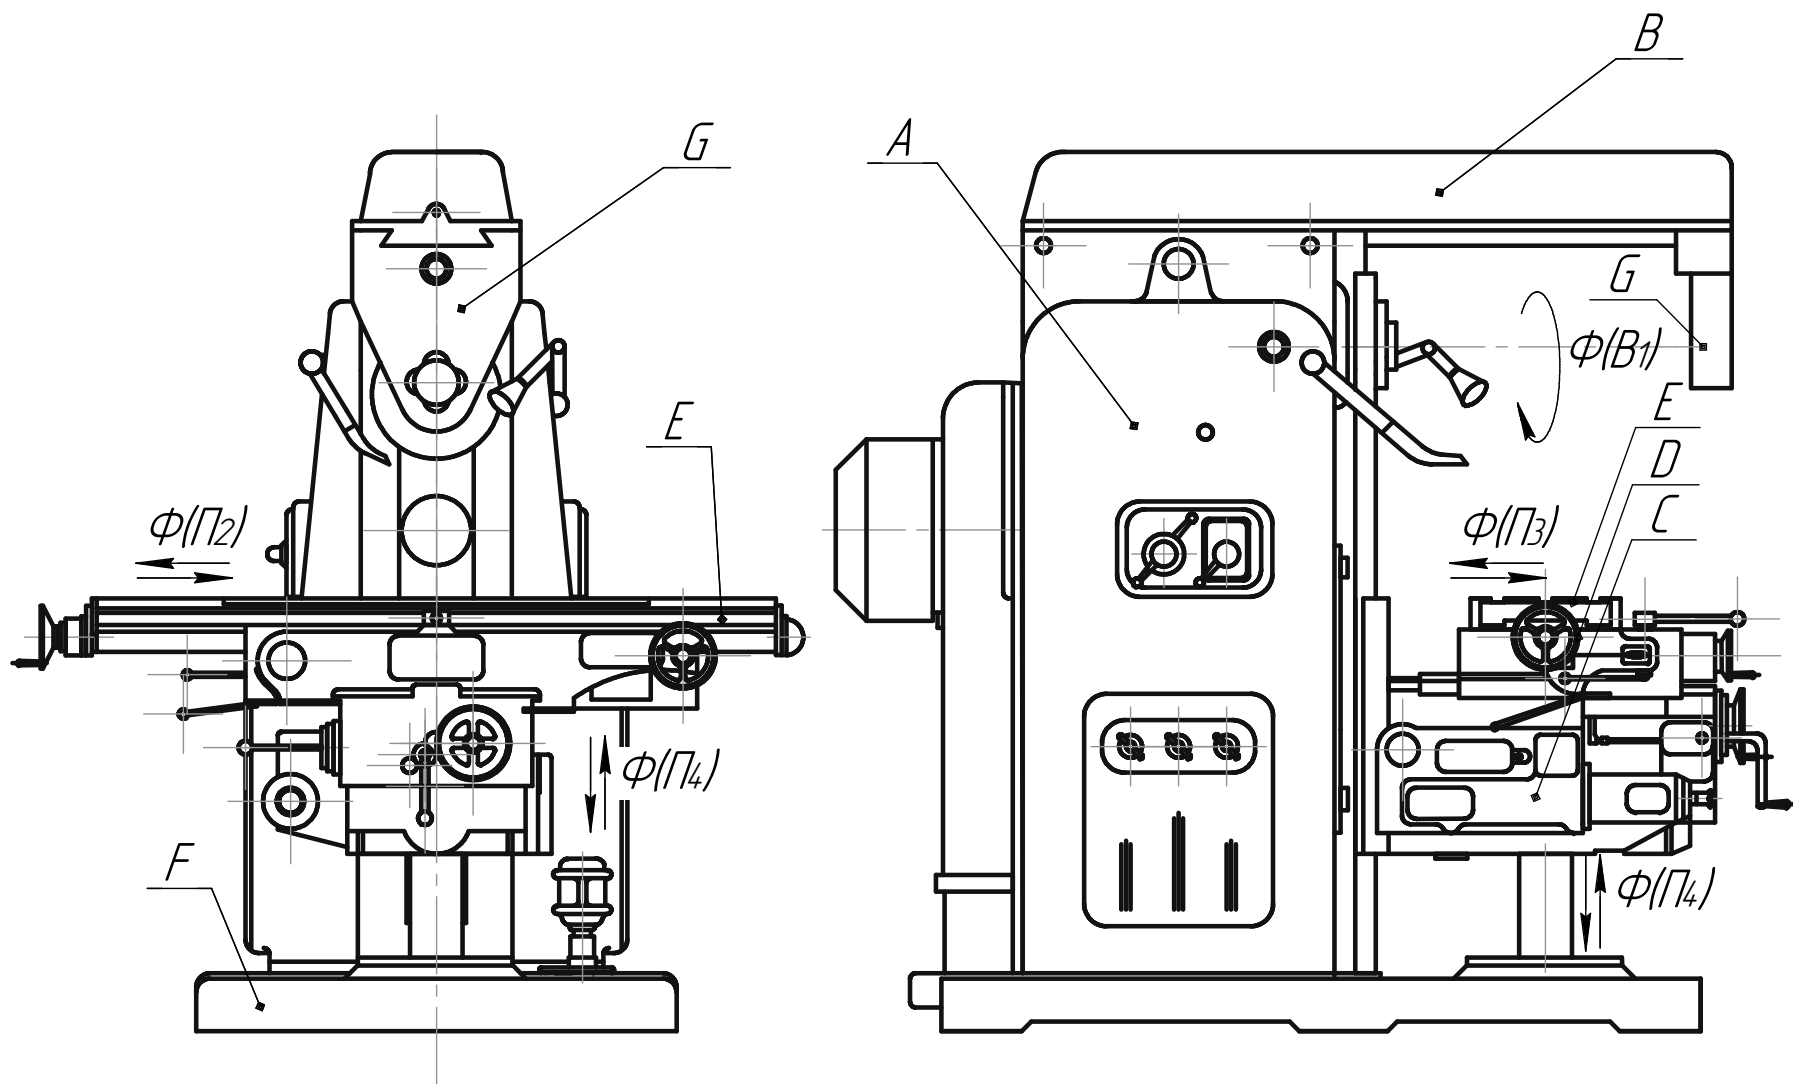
Загальний вигляд консольного горизонтально-фрезерного верстата 6Н82Г
